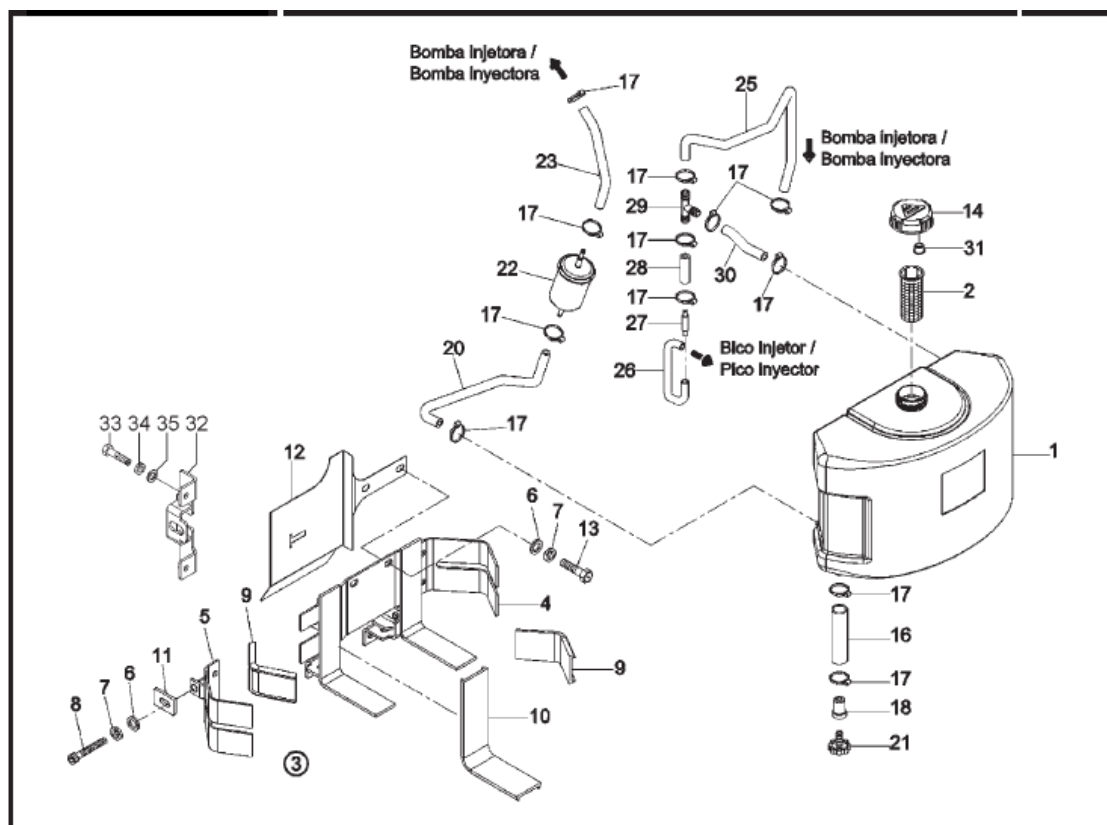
Conjunto tanque de combustível do motor Agrale M95W [41]
